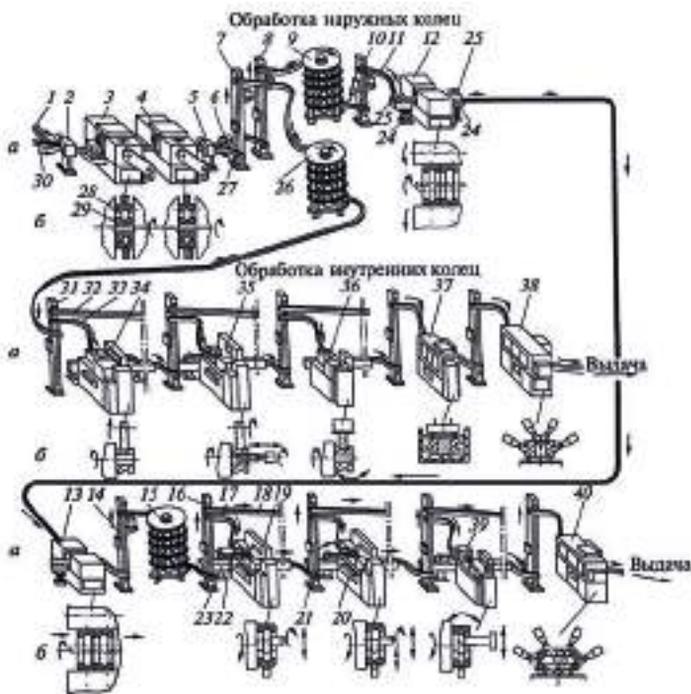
АЛ для шлифования колец шарикоподшипников:
